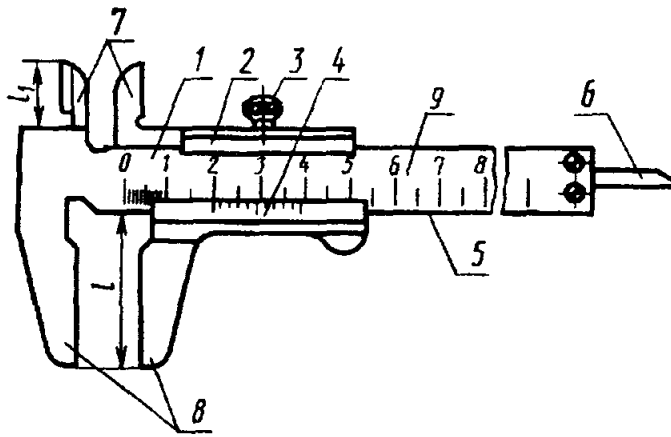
1- штанга; 2- рамка; 3- зажимаючий елемент; 4- ноніус; 5- робоча поверхня штанги; 6- глибиномір; 7- кромкові з вимірювальними поверхнями губки для вимірювання внутрішніх розмірів; 8- губки з плоскими вимірювальними поверхнями для вимірювання зовнішніх розмірів; 9- шкала штанги
